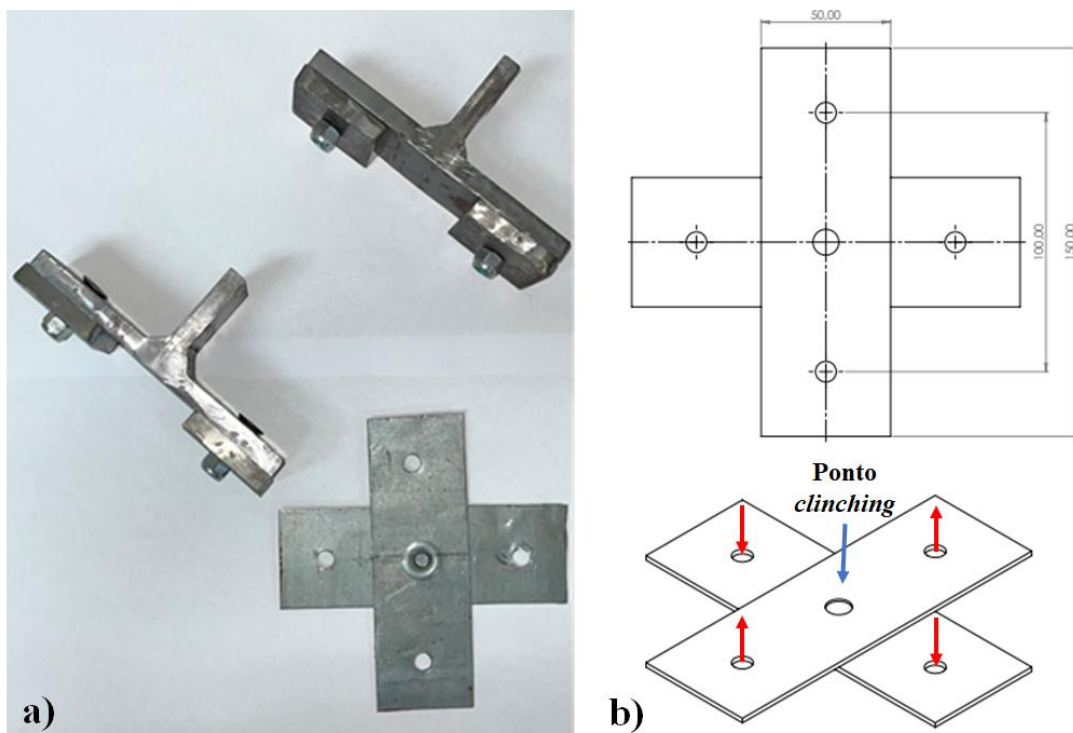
Ensaio de Arrancamento: a) dispositivo utilizado no teste e b) cinemática do ensaio.
